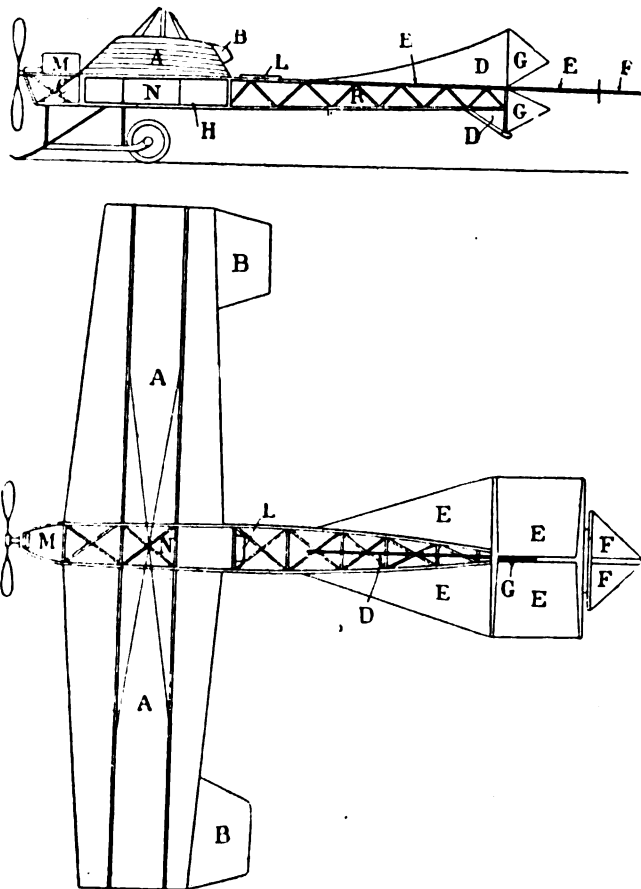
Monoplano Antoinette. - Pianta e sezione.
